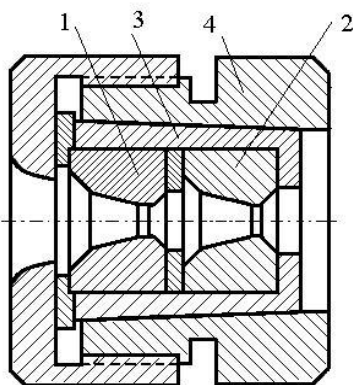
Сдвоенная волока: 1 – напорная волока; 2 – рабочая волока; 3 – разрезная втулка; 4 – корпус.
